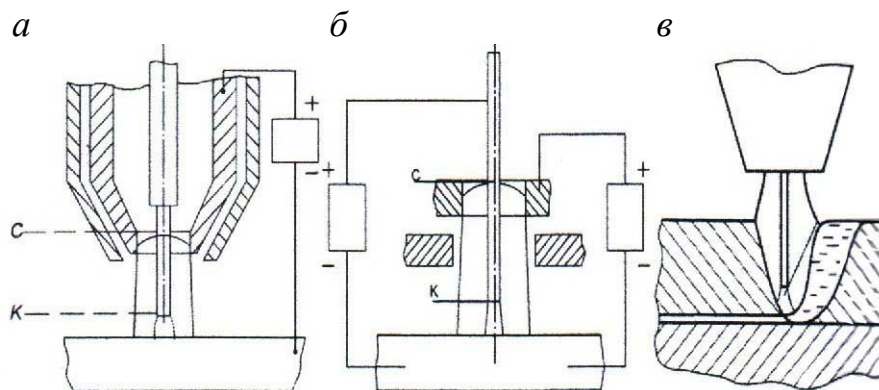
Схемы комбинированной плазменной сварки:
